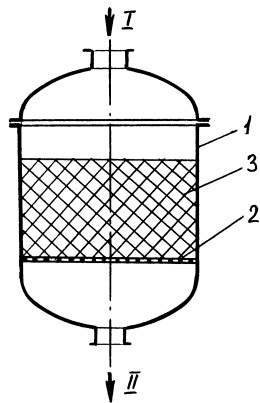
Газовий фільтр з плоскою фільтрувальною перегородкою: 1 – корпус; 2 – перфорована решітка; 3 – дрібнозернистий матеріал; I – вихідна газова суміш; II – очищений газ
